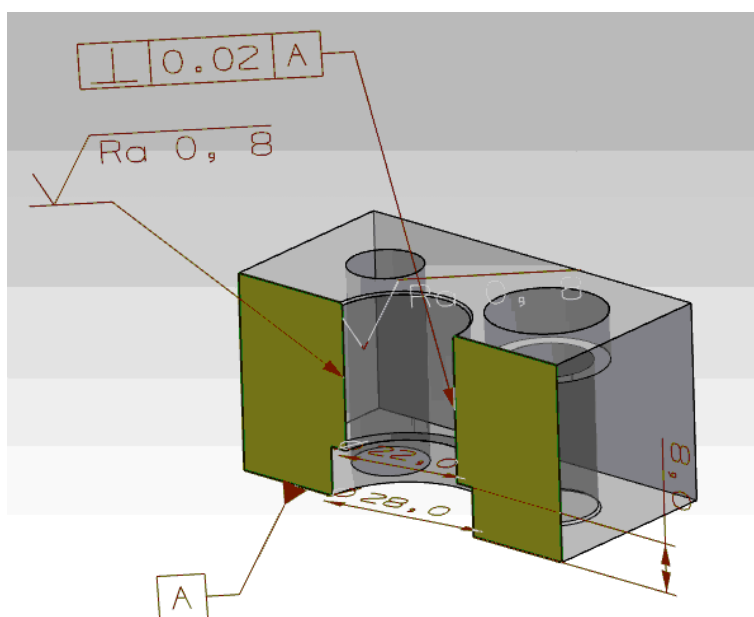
Допуски формы и шероховатость поверхности
